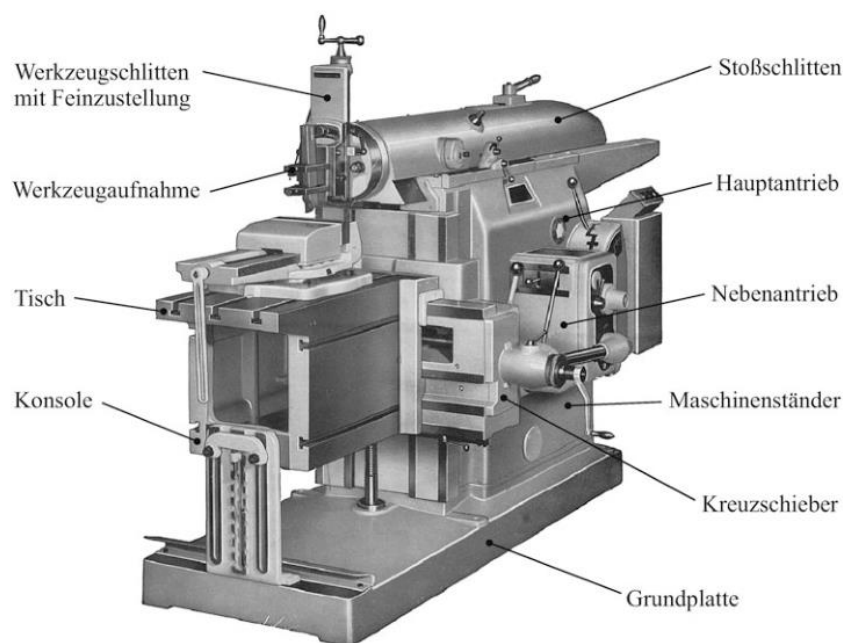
Teile der horizontalen Stoßmaschine [12]
